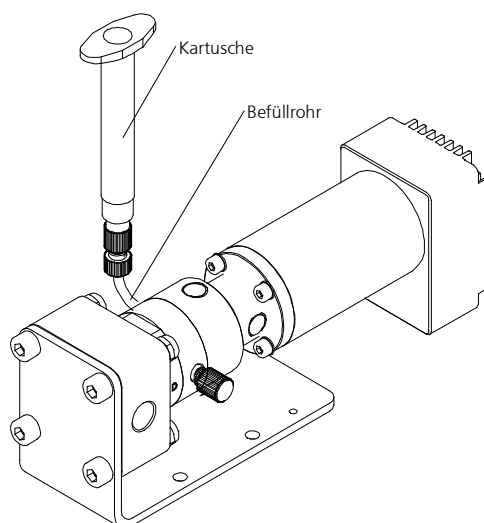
Aufbau der Mikrozahlringpumpe mit Sperrdichtungsmodul am Beispiel der mZR-7245 (Darstellung mit Anschlussset Sperrdichtung Variante 2)
